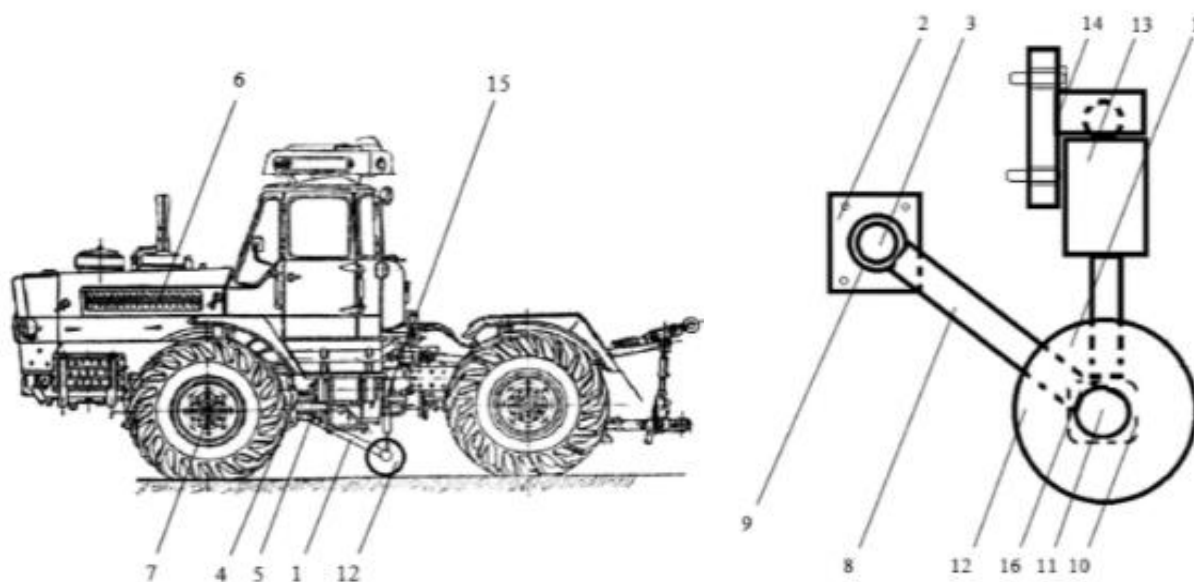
Дискаторный разуплотнитель следа колёсного трактора:
